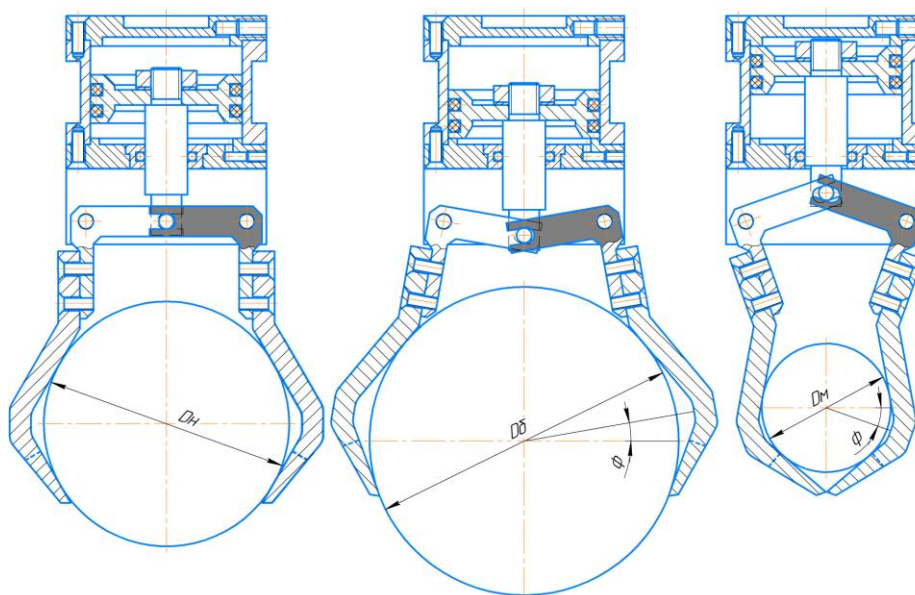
Типові умови затиску циліндричної деталі:
